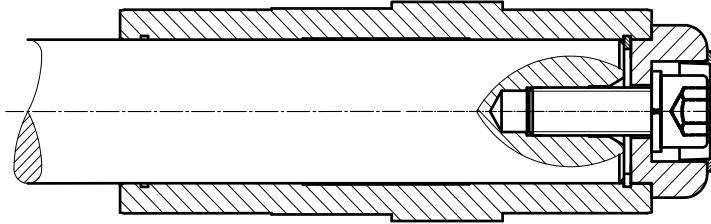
Getriebe auf Welle ohne Anlageschulter mit Befestigungselement befestigt
